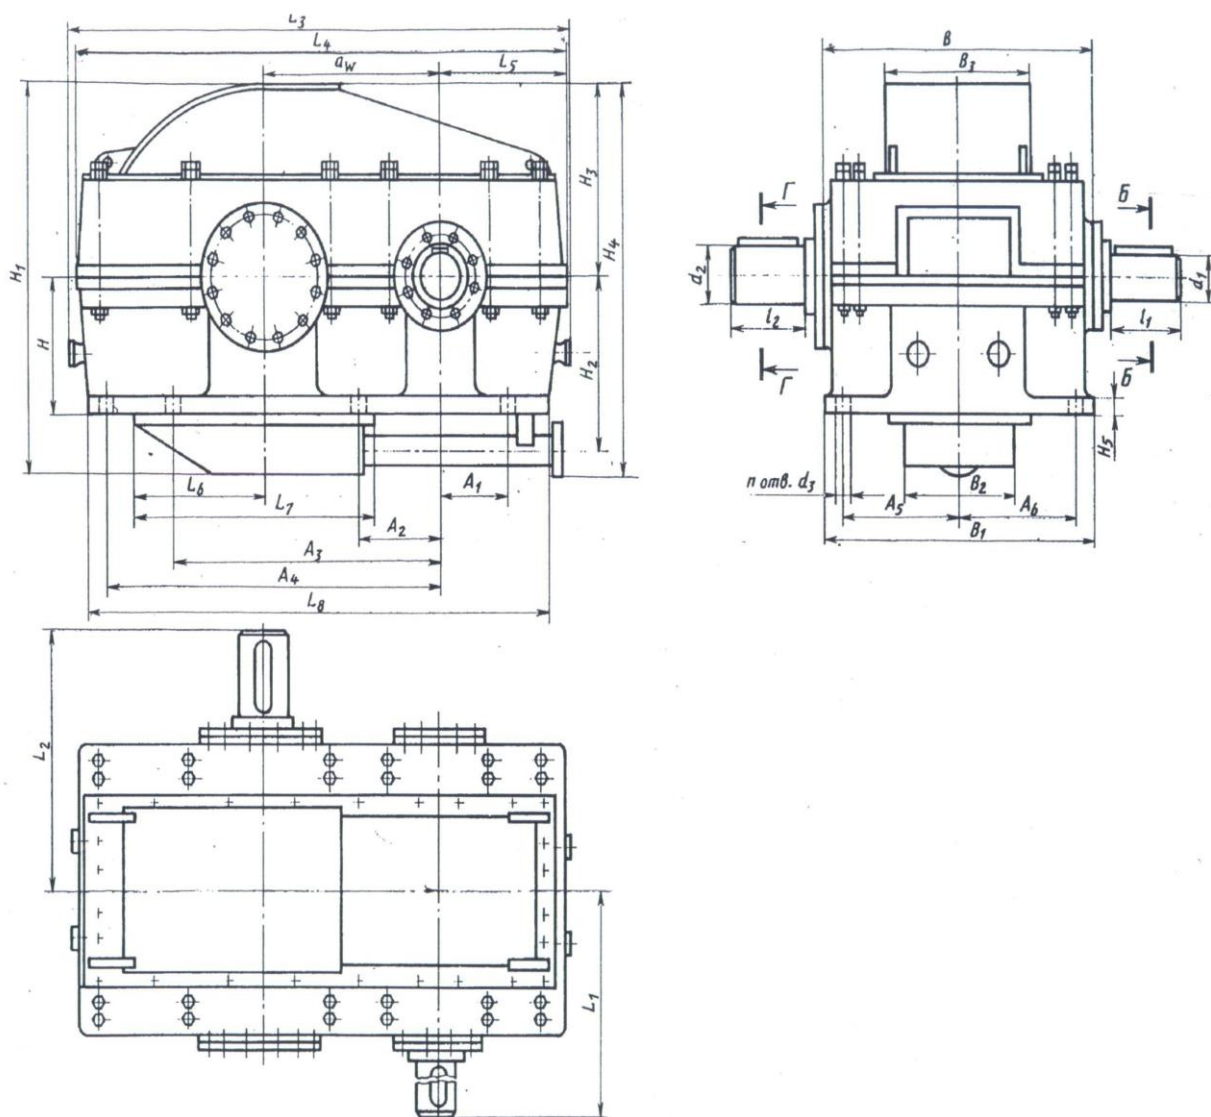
Габаритные и присоединительные размеры редуктора.
